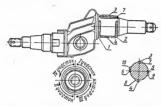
Восстановление коленчатой оси трактора ДТ-54.
